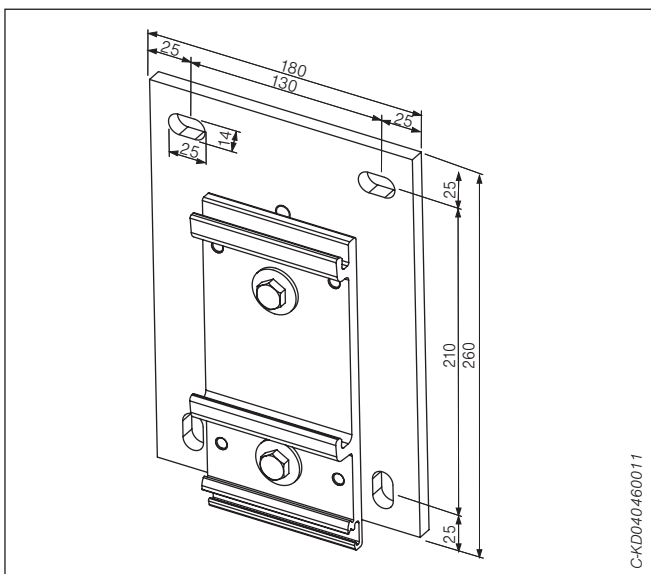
Consola tipo C – Fijación mural con placa de montaje pequeña
